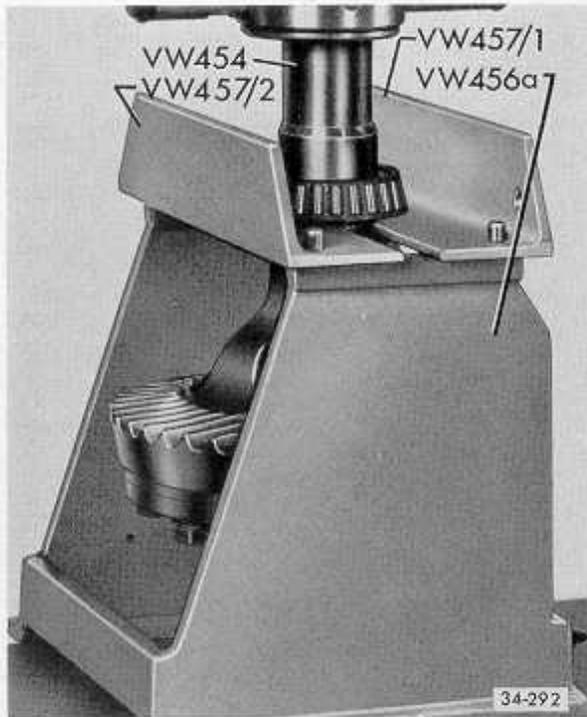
Innenring/Kegelrollenlager vom Gehäuse abpressen.
